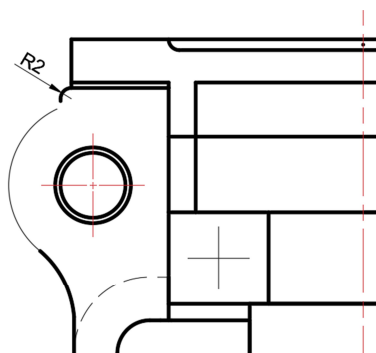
Дуга и радиус для формирования выступающей бобышки
